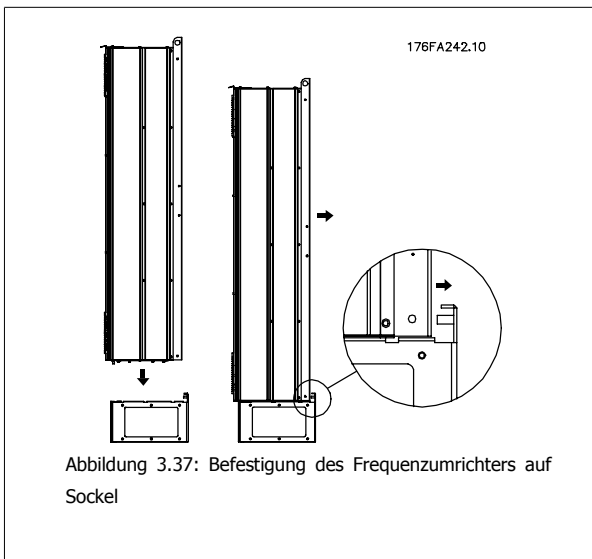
Befestigung des Frequenzumrichters auf Sockel
